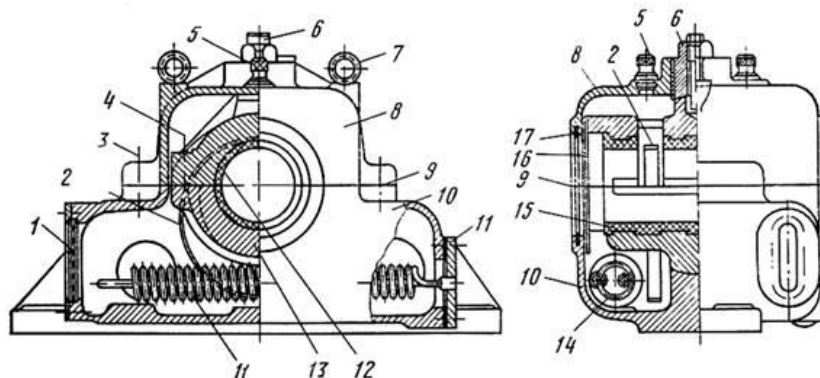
Подшипник дымососа с самоустанавливающимися вкладышами и кольцевой смазкой
